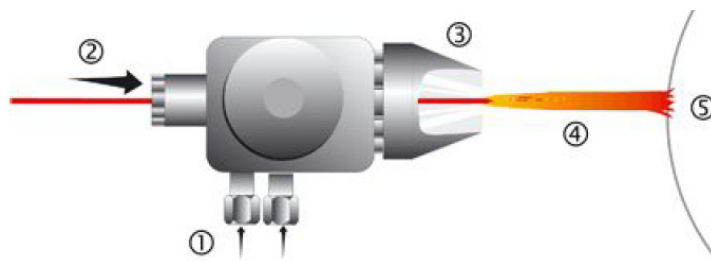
Схема установки газопламенного напыления проволоки или стержня
